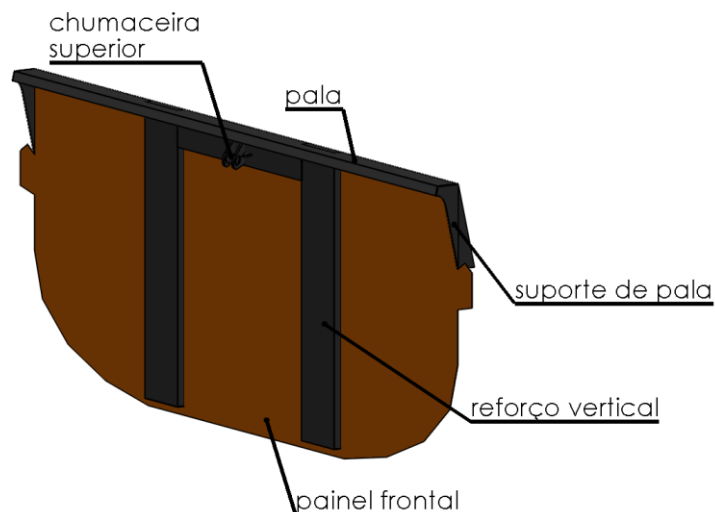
Taipal Frontal – vista isométrica – descrição
